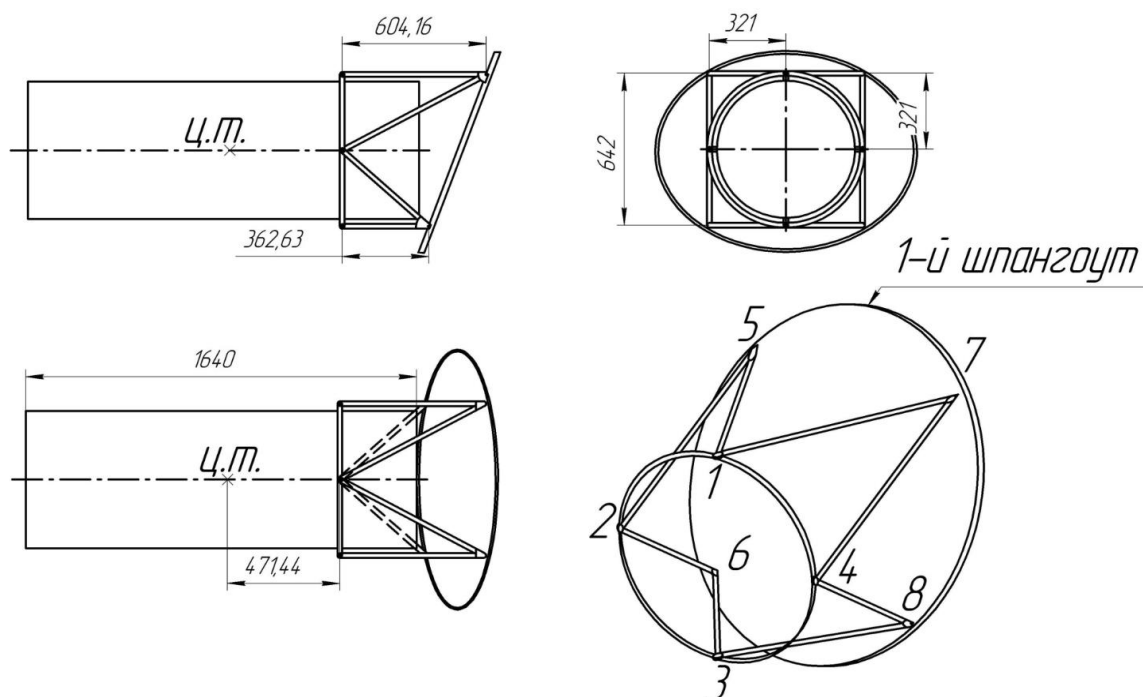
Общий вид фермы навески двигателя ВК-800С
